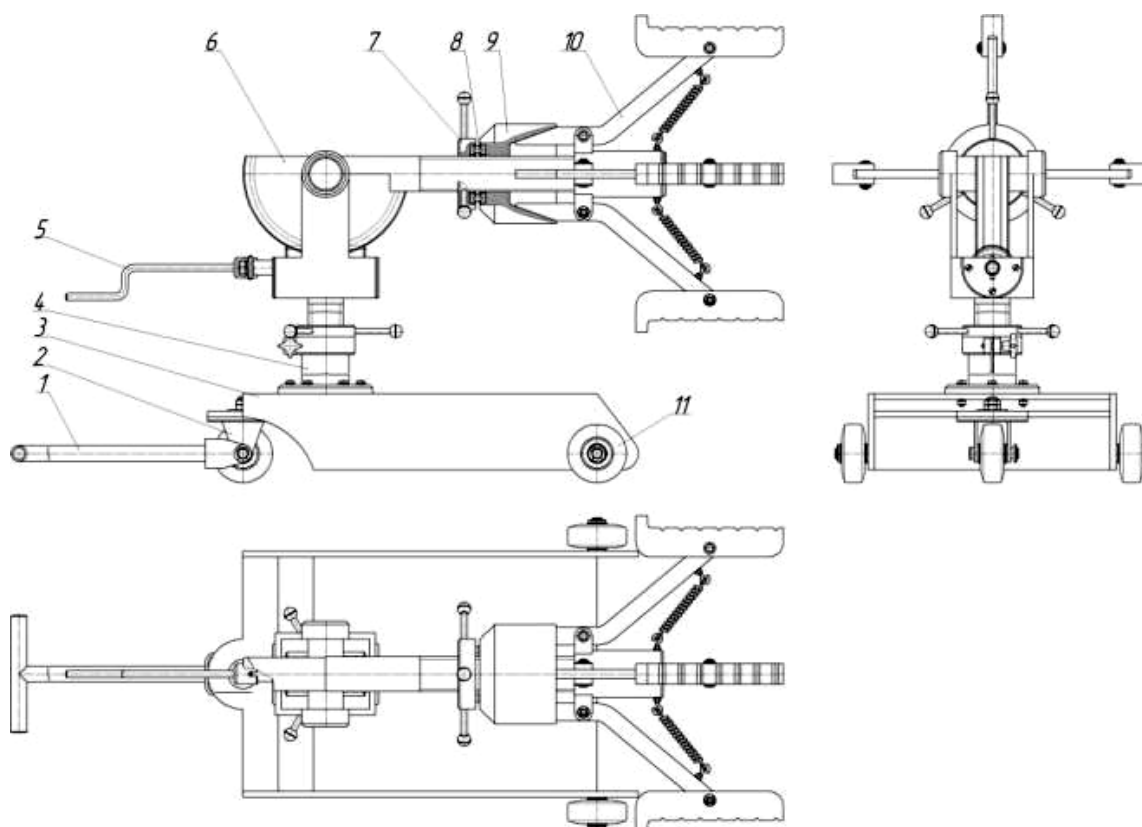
Тележка для снятия и установки колес: 1 – рукоятка; 2 – опора поворотного колеса; 3 – основание; 4 – механизм подъема; 5 – ручка; 6 – механизм поворота; 7 – гайка; 8 – подшипник; 9 – гайка нажимная; 10 – механизм фиксации колеса; 11 – колесо основное.
